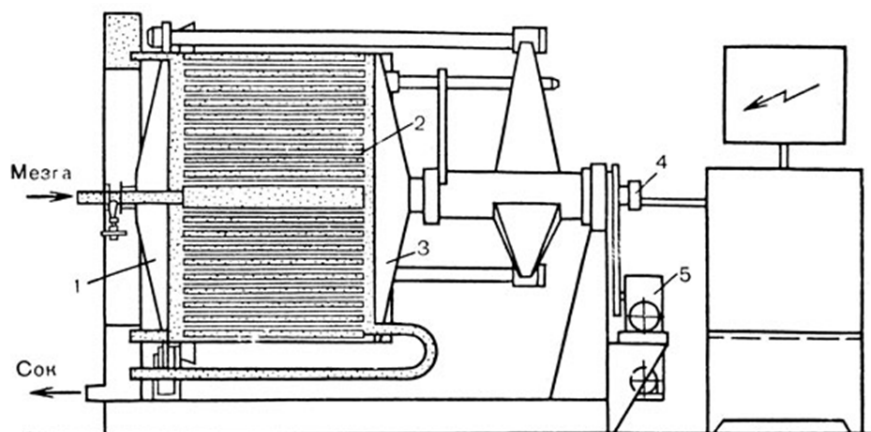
Пресс 'Бухтер НР': 1 - неподвижный диск; 2 - дренажный тросс; 3 - подвижный диск; 4 - вал; 5 – привод
